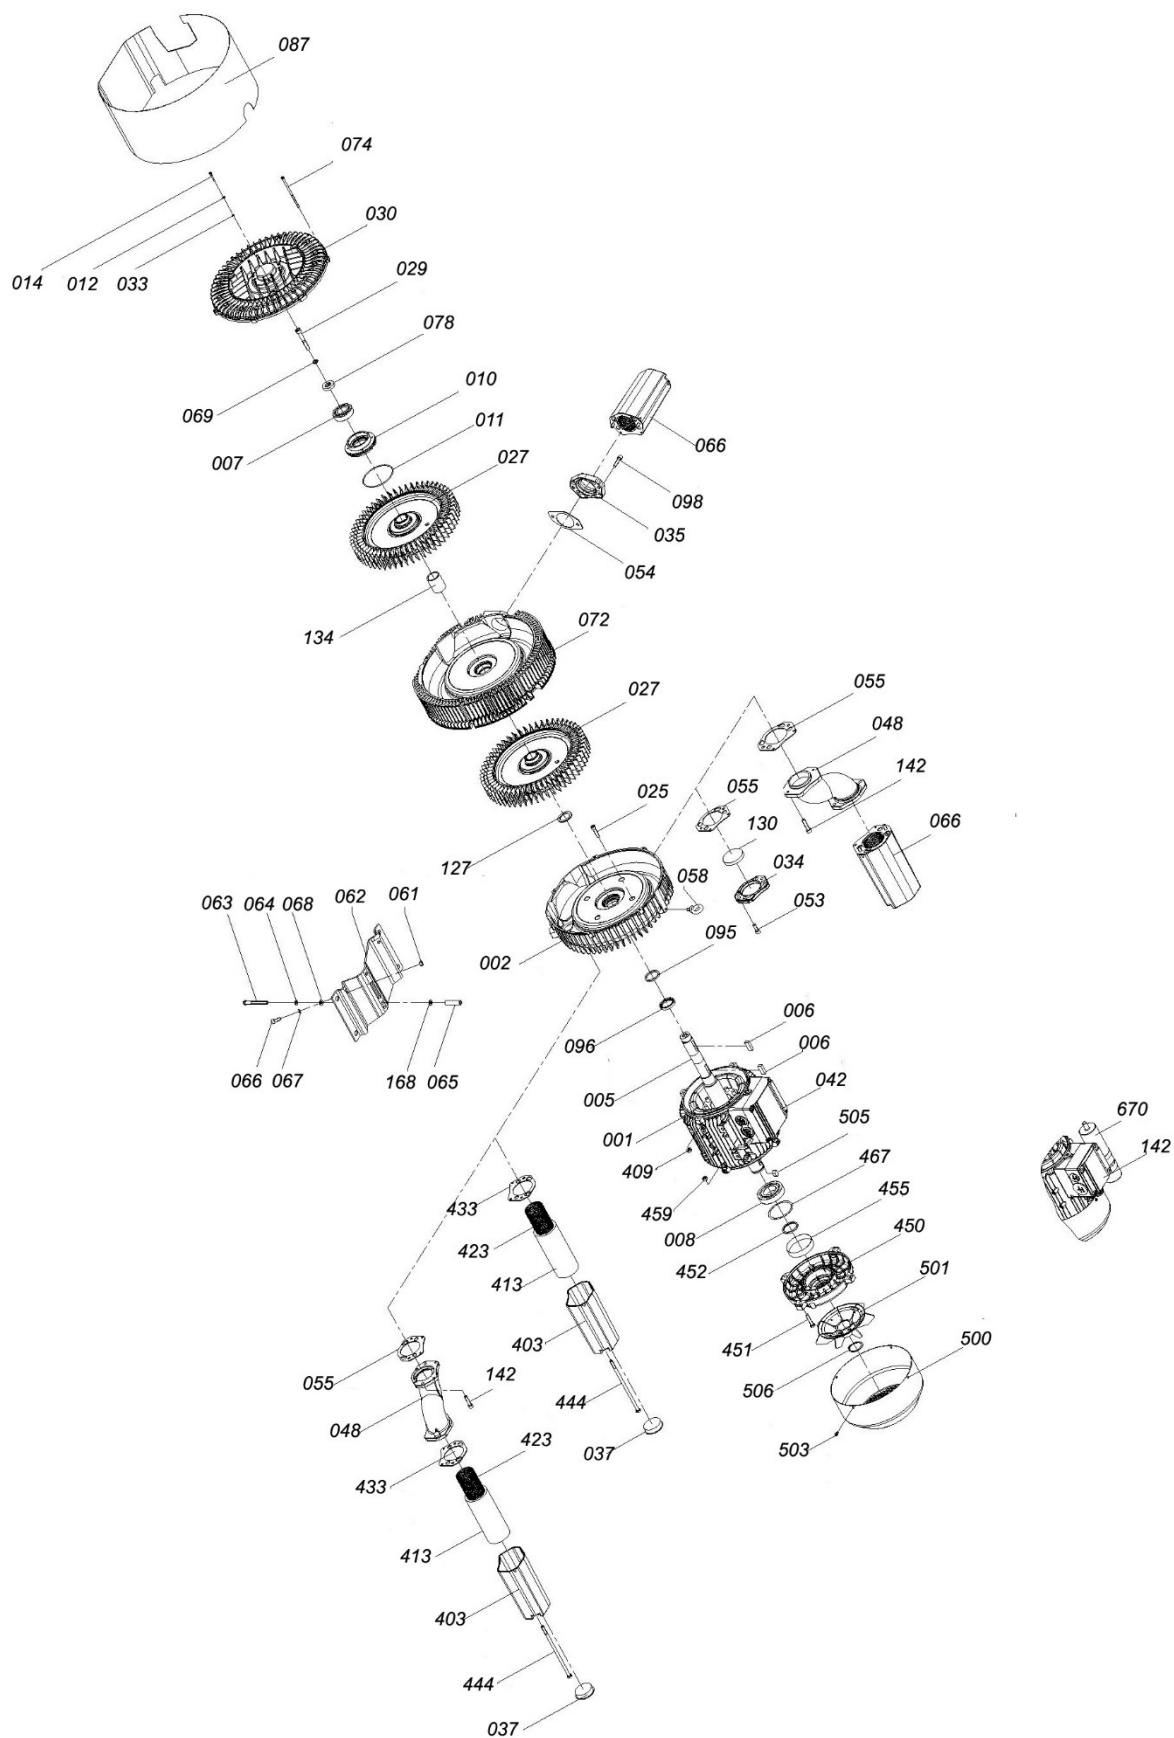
Деталировка двухступенчатых воздуховок 2RB
